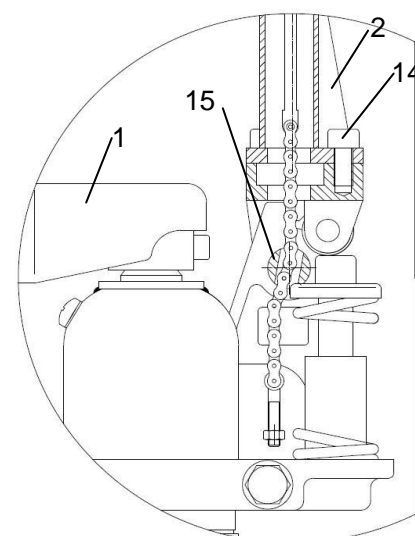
Veduta laterale ER-D assemblaggio tiller
